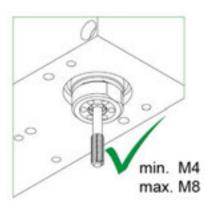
Einsatzbereich Gewindeformwerkzeug
